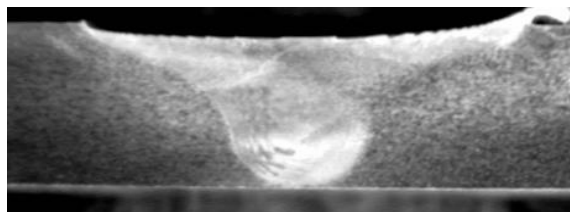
6061-T6 铝合金搅拌摩擦焊接头横截面宏观形貌
